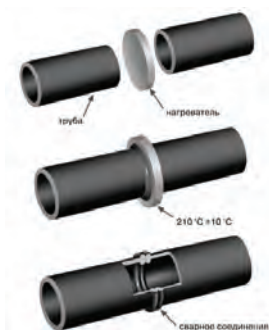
Схема стыковой сварки полиэтиленовых труб
